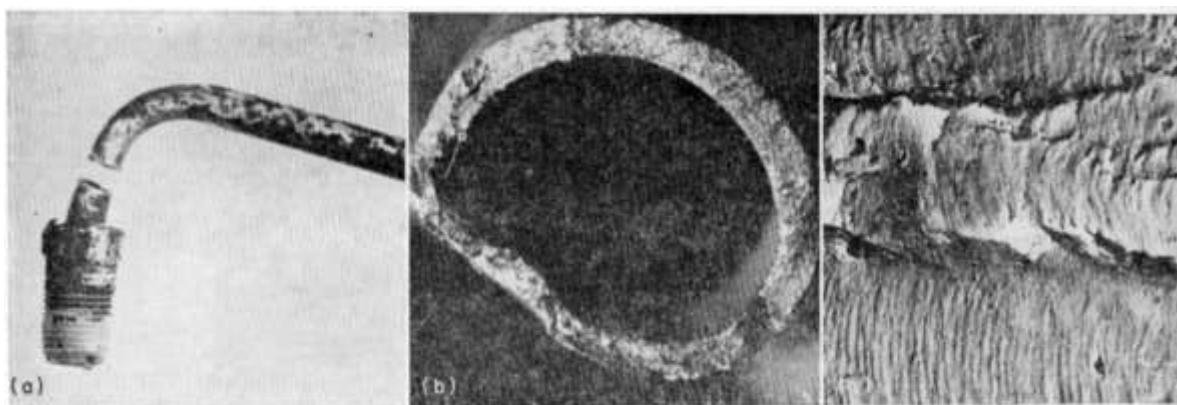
Трубка тормозного автомобильного цилиндра из низкоуглеродистой стали, разрушившаяся в результате резонансной вибрации: а – общий вид разрушенного изделия. $\times 0,9$; б — поверхность разрушения. $\times 9$; с — усталостные бороздки на поверхности разрушения. ПЭМ, пластиково-угольная реплика. $\times 6000$
